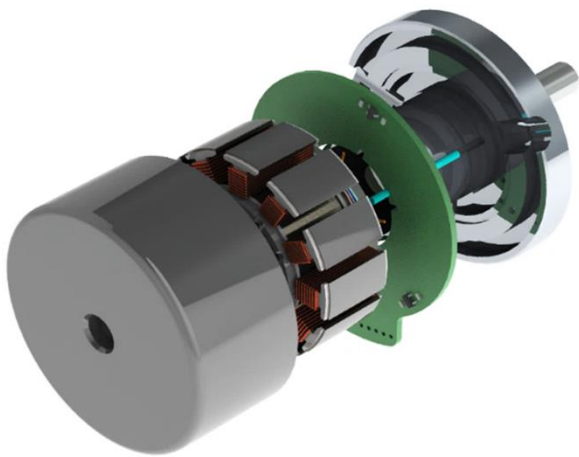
3D-Explosionszeichnung eines Motors vom Typ geschlossener Rotor.
